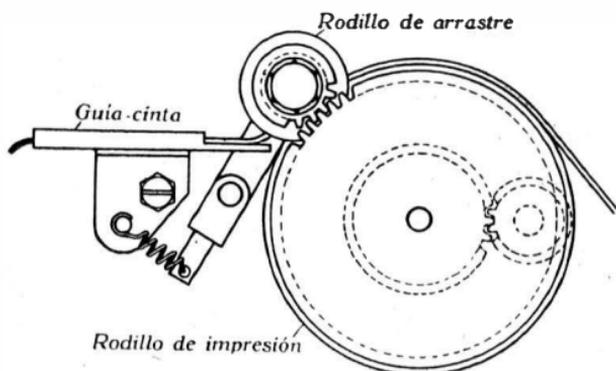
Rodillos de impresión y de arrastre del aparato Morkrum
